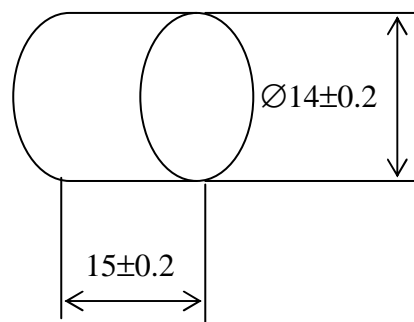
Dimensions de l'éprouvette cylindrique, mm.
